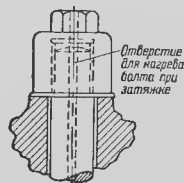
Верхняя часть стяжного болта фланцев корпуса турбины.
